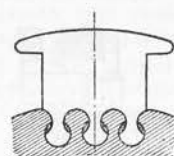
Poli executați din tole cu prindere în T multiplu.
